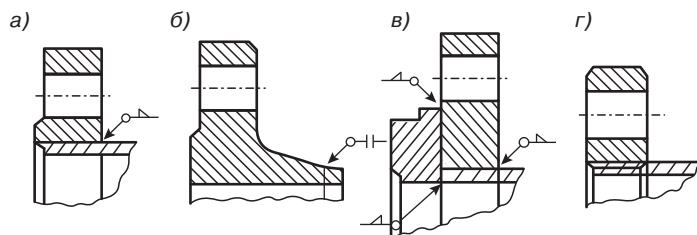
Конструкции фланцев: а — плоские приварные; б — приварные встык; в — свободные на приварном кольце; г — резьбовые
